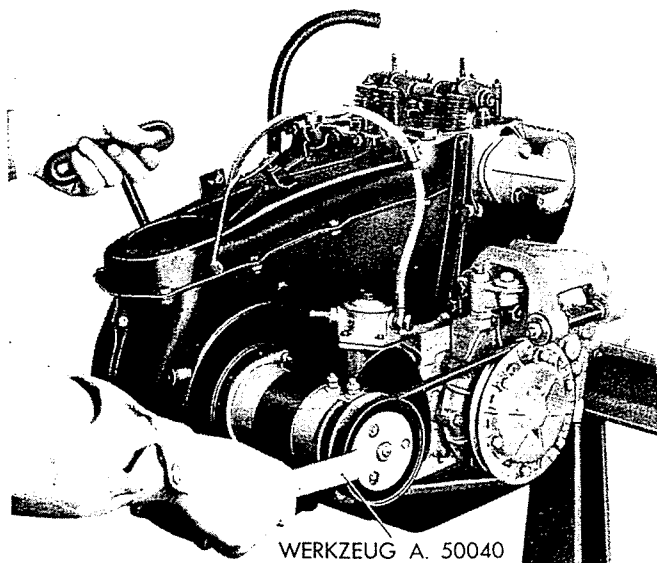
Werkzeug A. 50040 zum Festhalten der Lichtmaschinenwelle beim Ausbau des Gebläserads.
